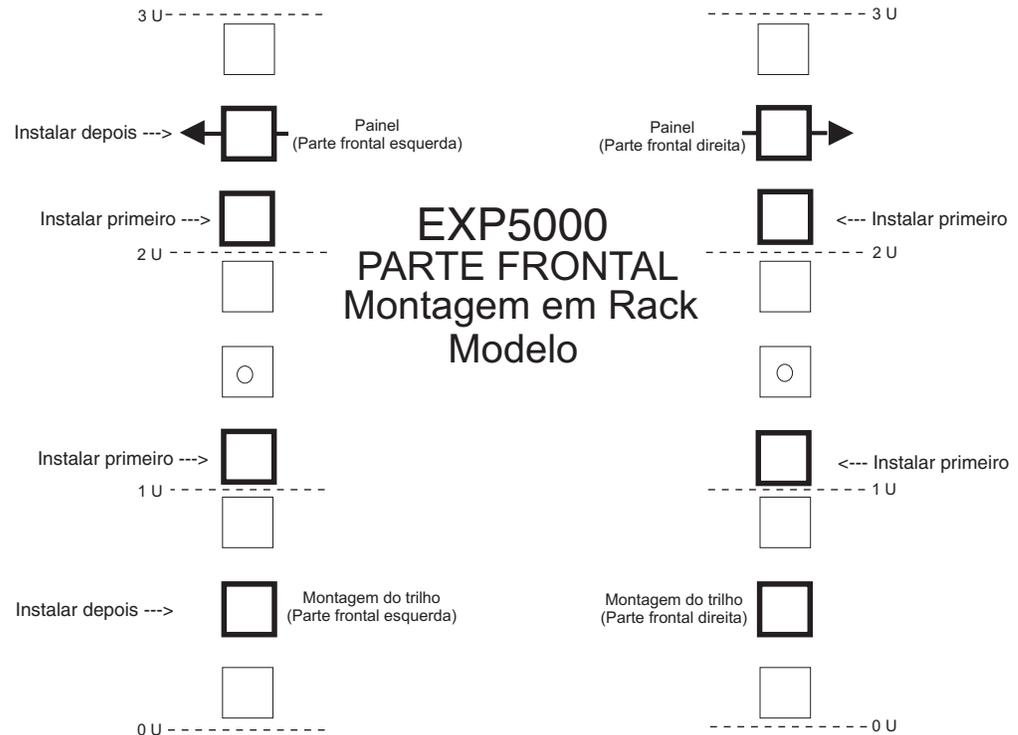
Modelo de Montagem da Parte Frontal do Rack
